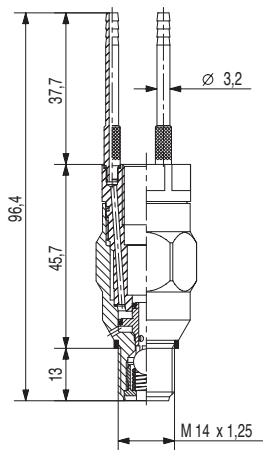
Zweiweg-Umschaltadapter Typ 737
